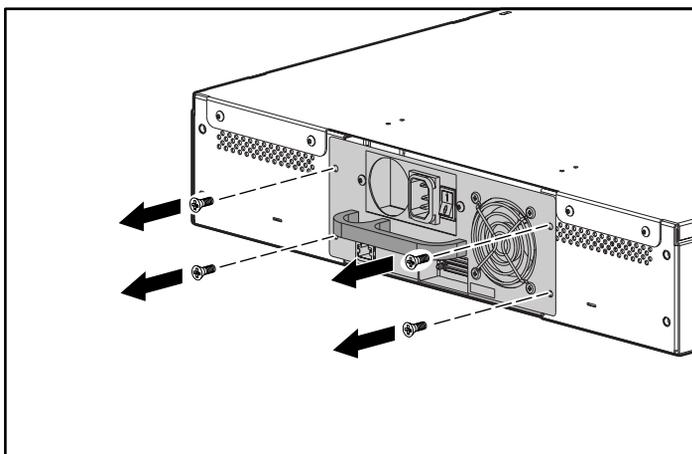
Entfernen der Schrauben an der Rückseite des Gehäuses
